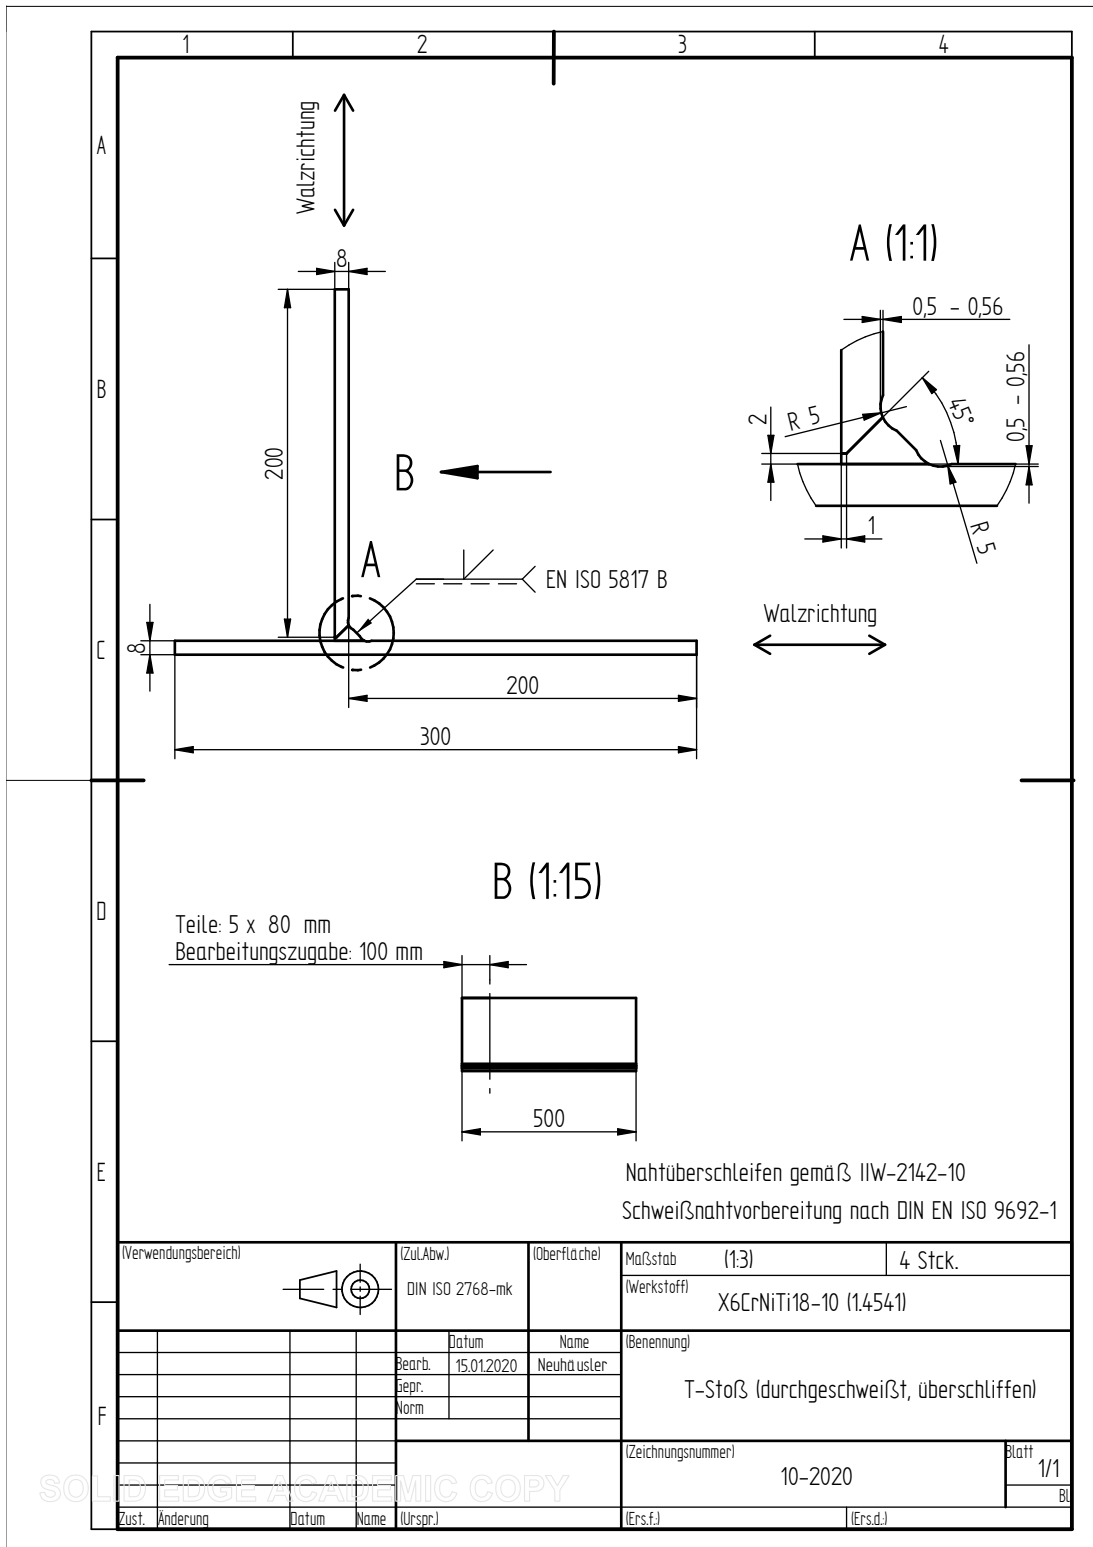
Fertigungszeichnung für die T-Stoß Proben aus 1.4541 [67].
